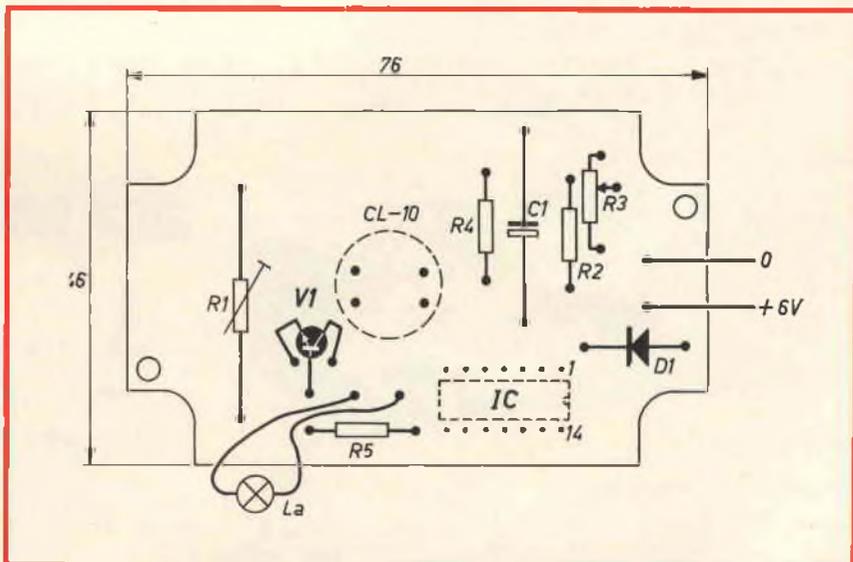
Circuito stampato visto dal lato componenti del rivelatore di gas.
